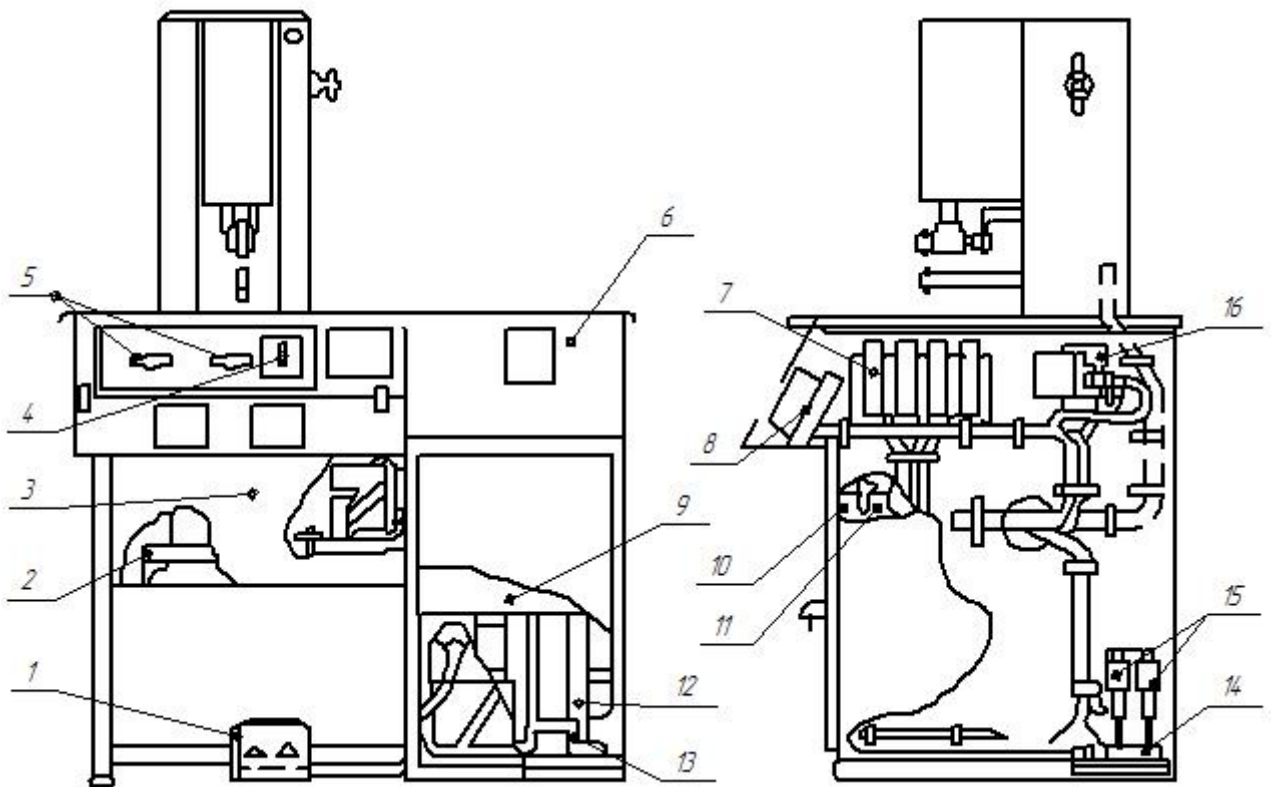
Будова машини для шовного контактної зварювання
